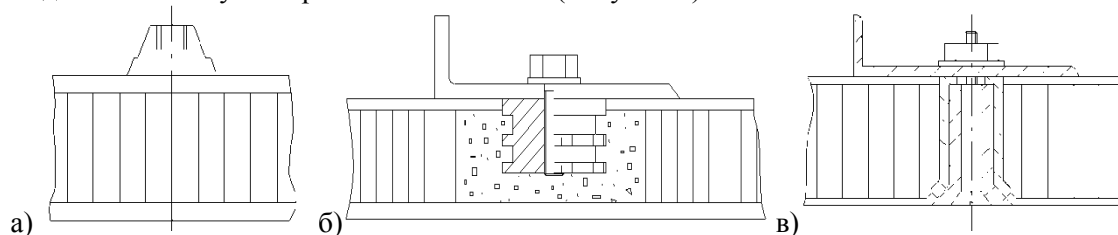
Способы закрепления вкладышей в отверстии трехслойной конструкции: а) сваркой; б) клеевым соединением; в) телескопическим соединением.
